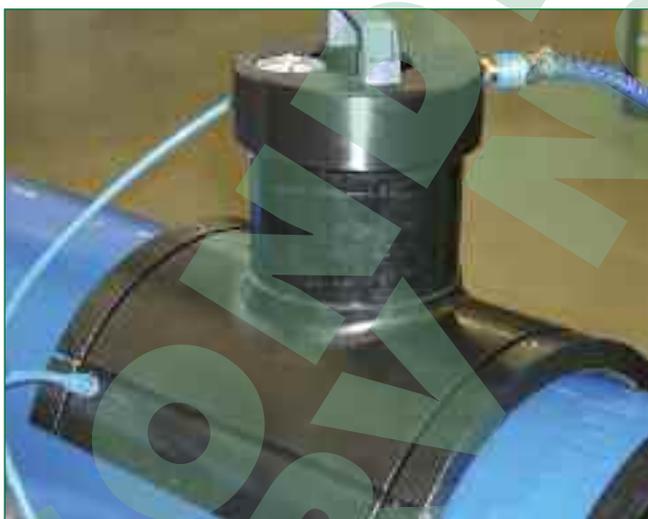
SA-XL während der Montage mittels Vakuumspanntechnik
